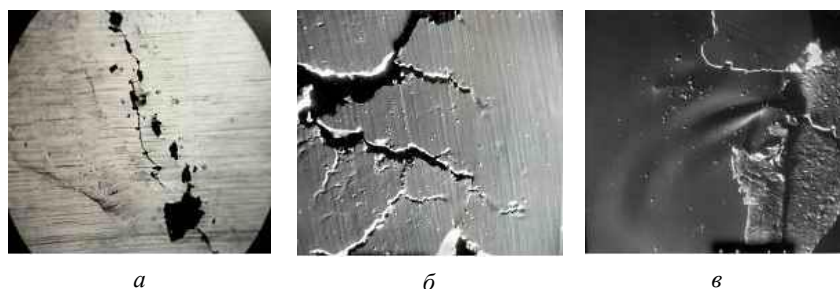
Дефекты заготовки бесслитковой прокатки:
